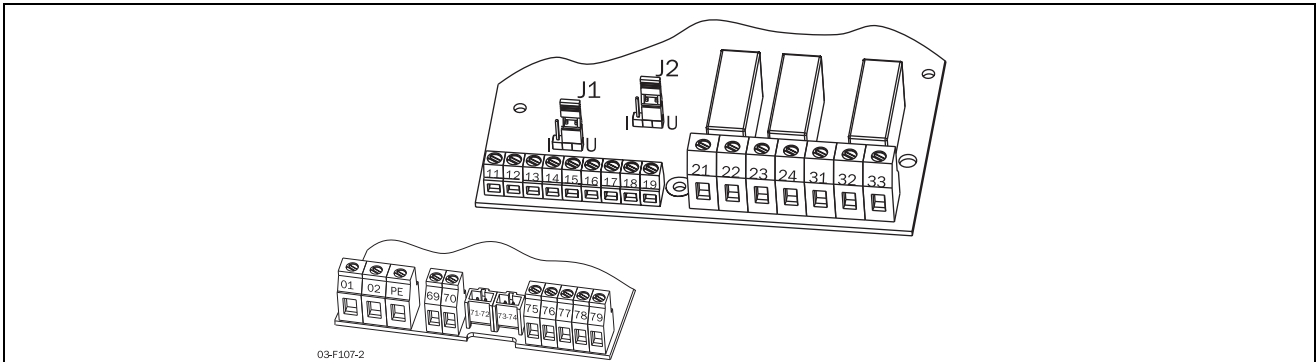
PCB (Steuerplatine) Anschlüsse.
